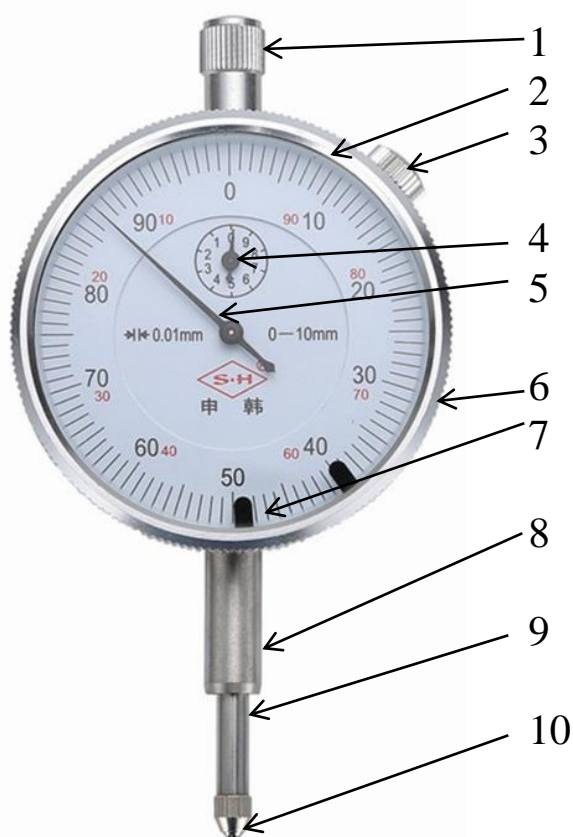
Индикатор часового типа: 1 – головка; 2 – корпус;
